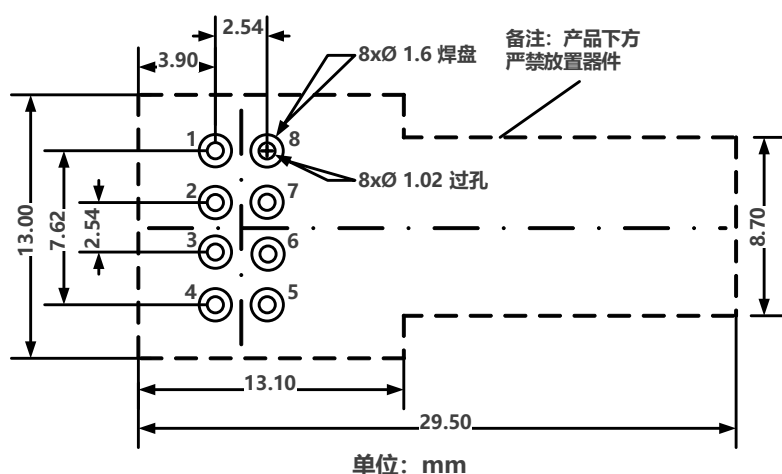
PCB Layout 设计推荐尺寸图（俯视图）
